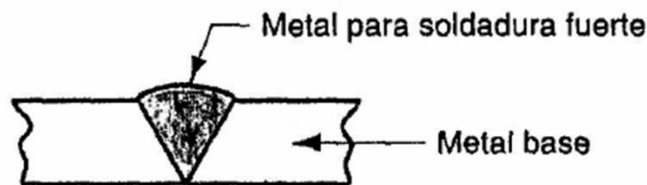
Soldadura Brazing por fusión. [5]
